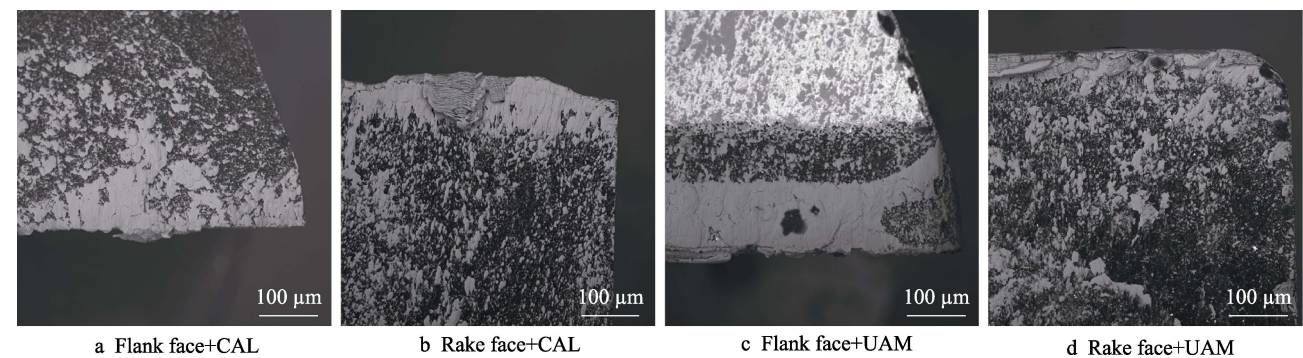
SLM 钛合金超声辅助和常规铣削下的刀具表面切屑黏结
